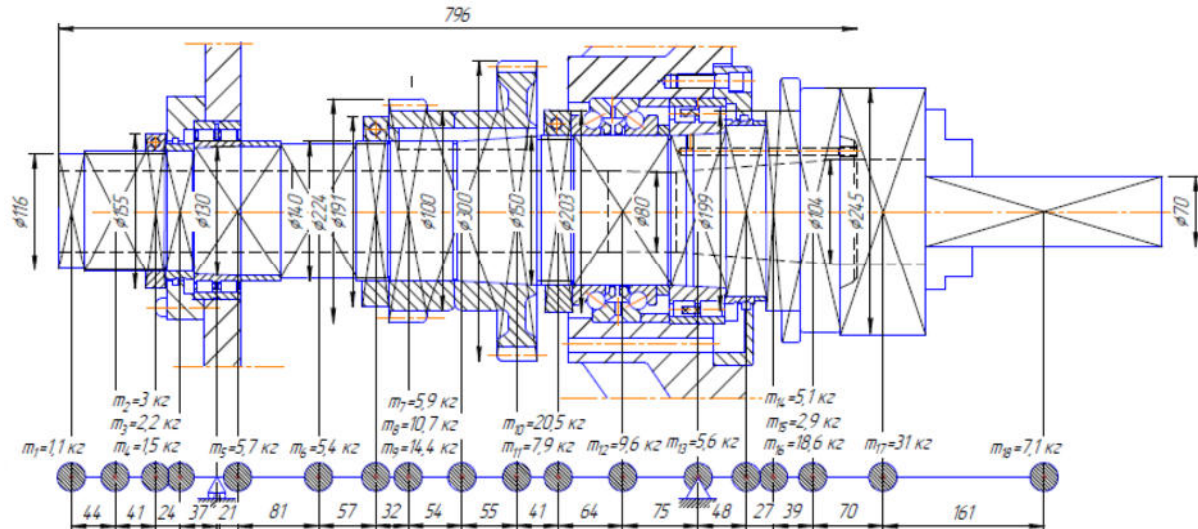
Шпиндельний вузол токарного верстата з ЧПК із затиснутою в токарному патроні заготовкою та його динамічна модель у вигляді пружної невагомої балки із зосередженими масами
